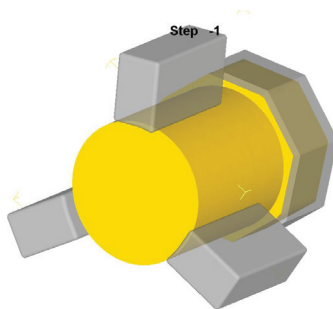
Твердотельная модель устройства для моделирования процесса профилирования заднего конца заготовки
